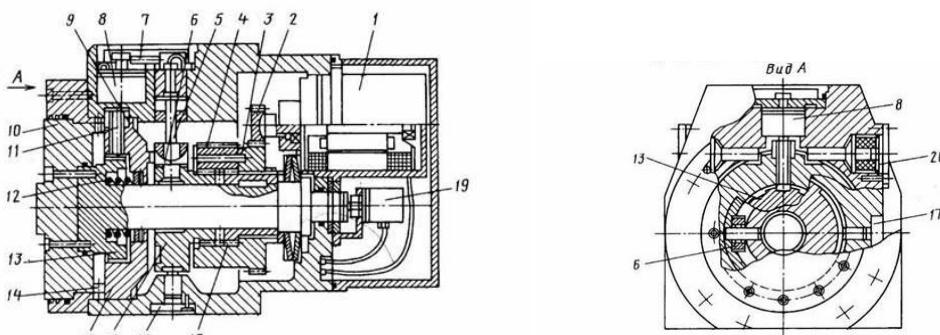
Конструкция электромеханической револьверной головки для невращающегося инструмента токарных станков
